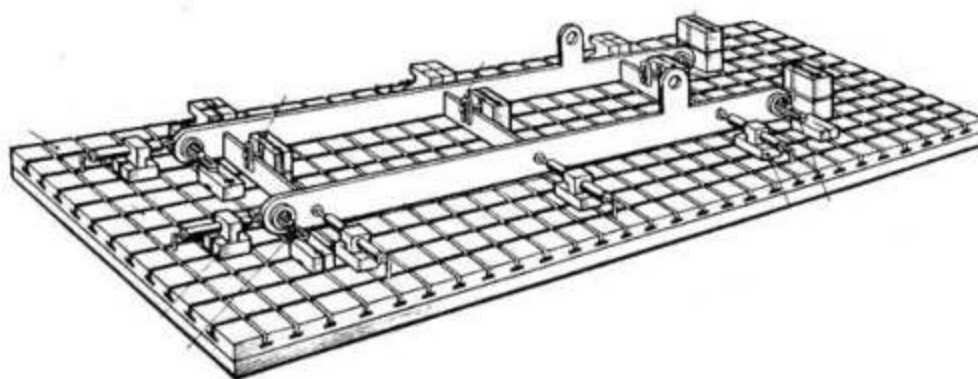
Рабочая поверхность для сборки и сварки
